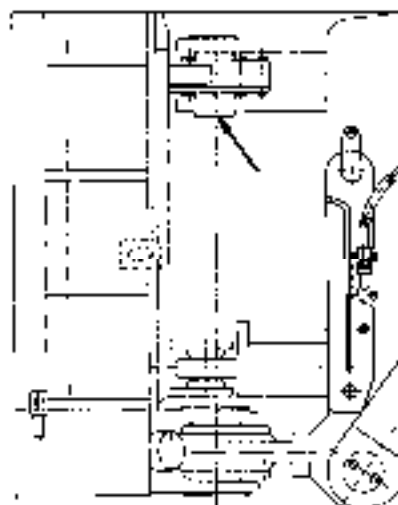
Масленка бочкообразного подшипника верхнего шарнира рамы
